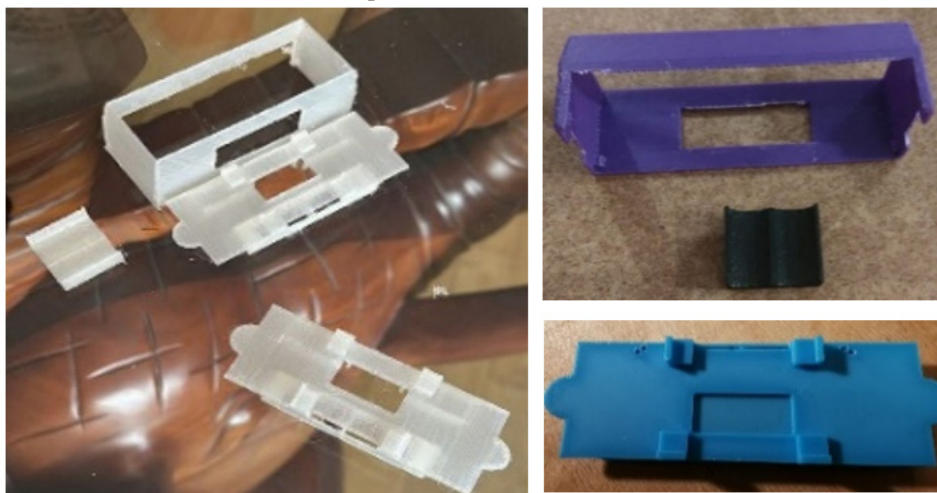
Напечатанные корпуса, основания, лотки для батарей
